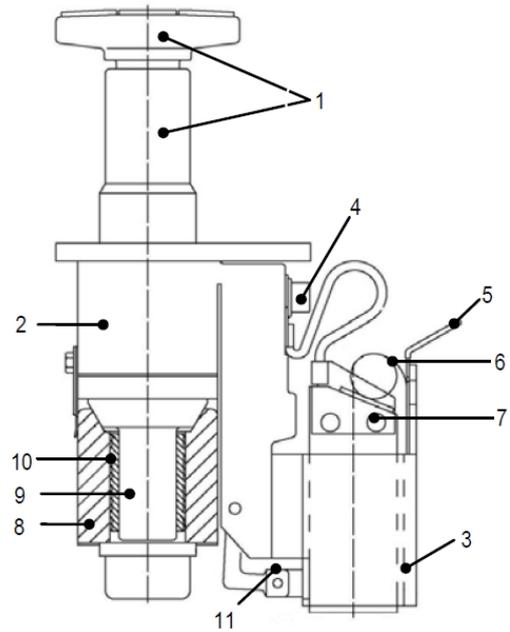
Внешний вид траверсы (полюса) ЩКА 1329
